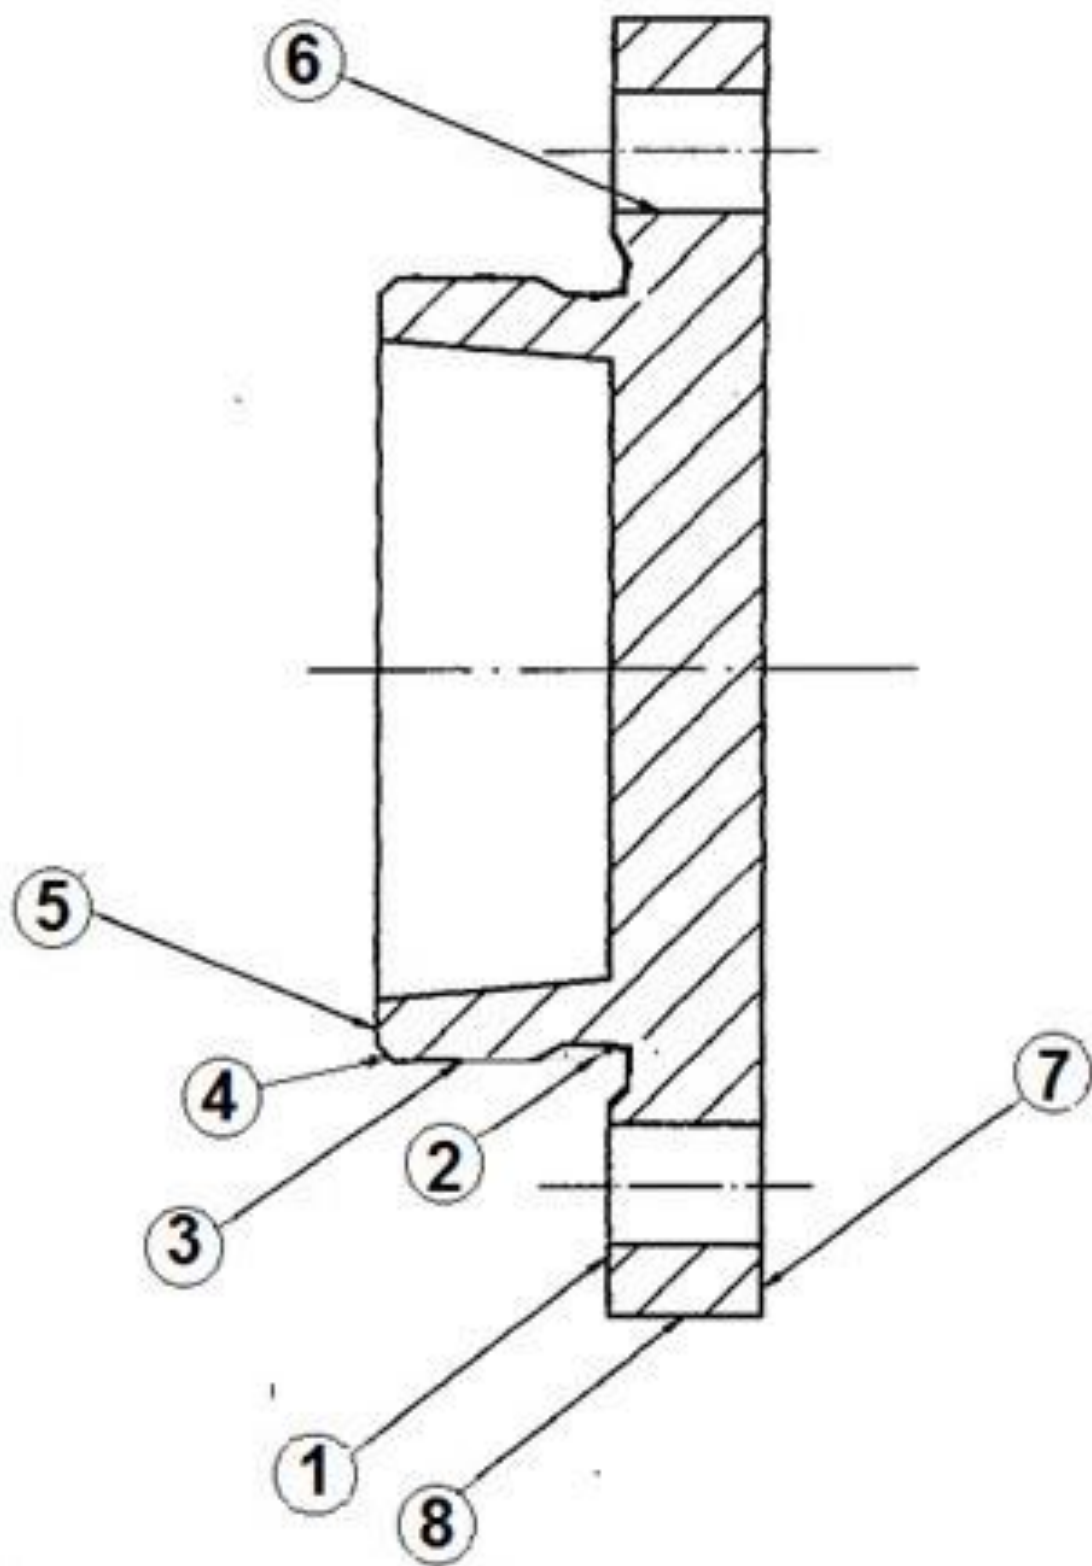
Эскиз крышки с номерами обрабатываемых поверхностей.
